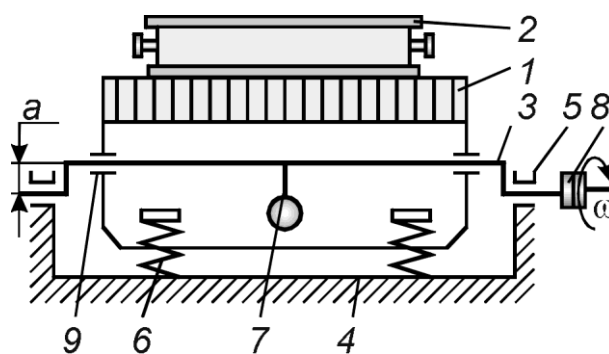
Схема вибивної ексцентрикової решітки: 1 – корпус решітки; 2 – опока; 3 – ексцентриковий вал; 4 – рама; 5, 9 – опори валу; 6 – амортизатори; 7 – дебаланс; 8 – муфта
